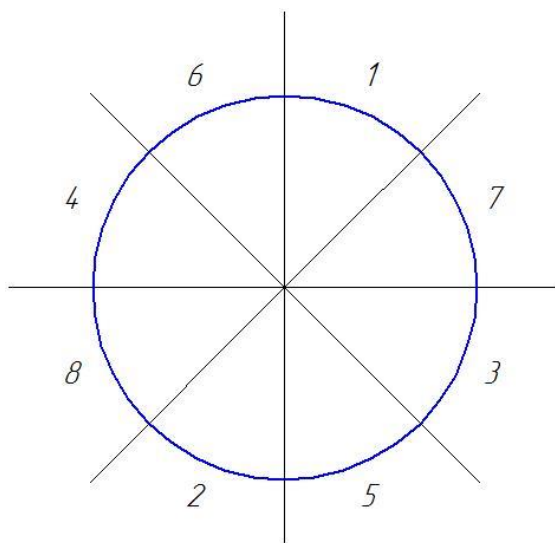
Схема сварки обечайки с телом конуса
